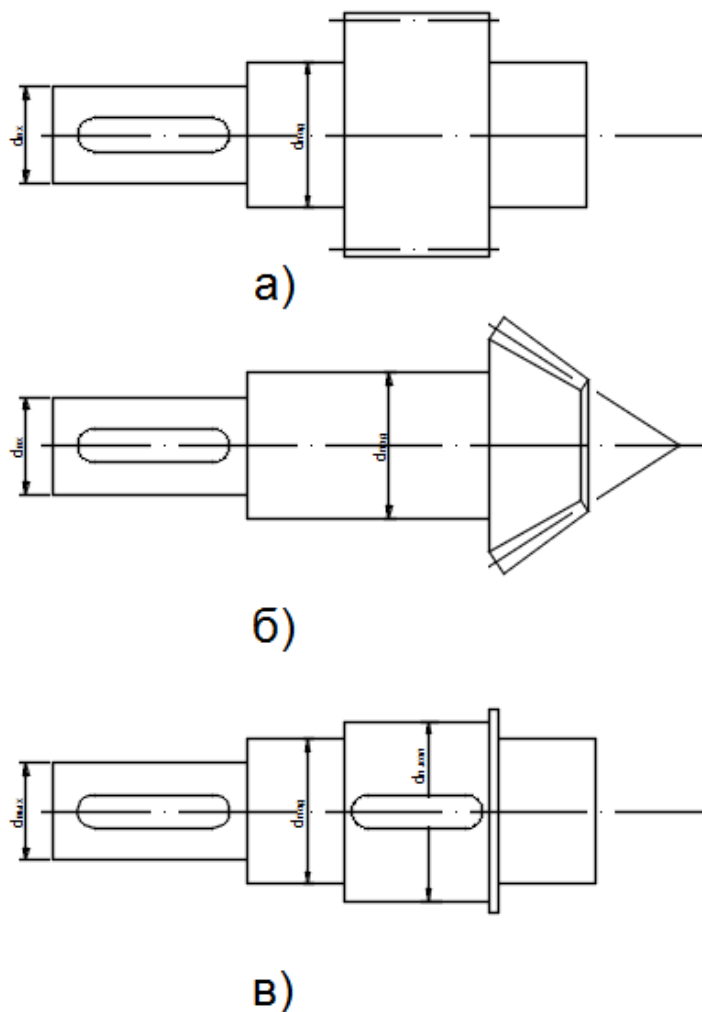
Эскиз вала: а – ведущий цилиндрический (червячный) вал; б – ведущий конический вал; в – ведомый вал.
